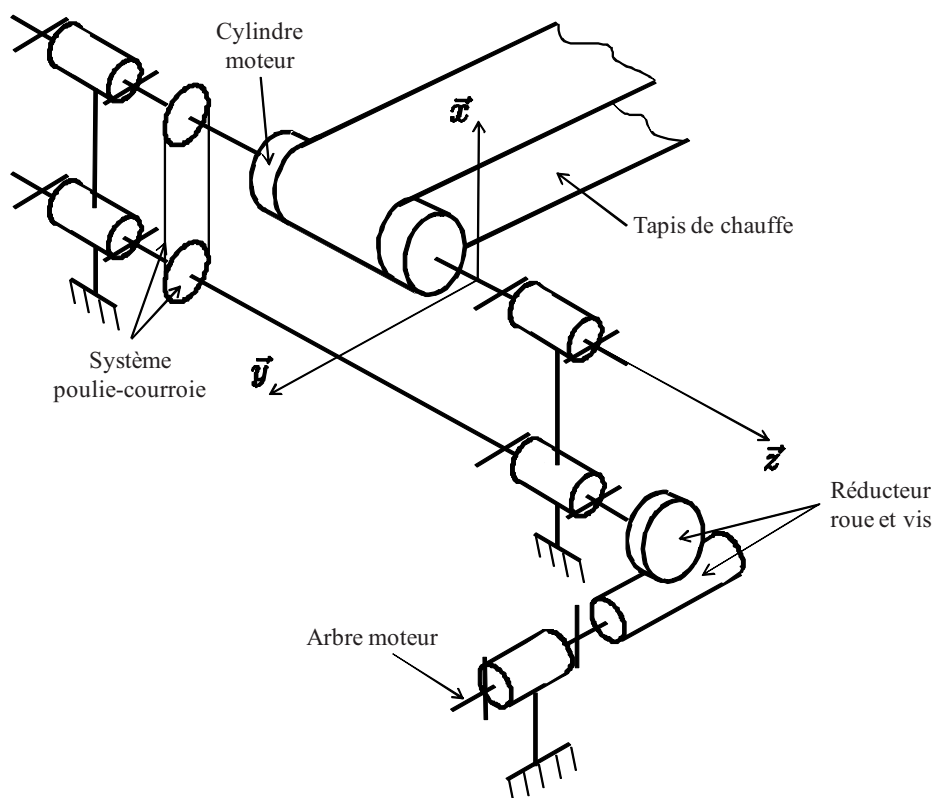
Ensemble moto-réducteur entraînant le cylindre moteur du tapis
